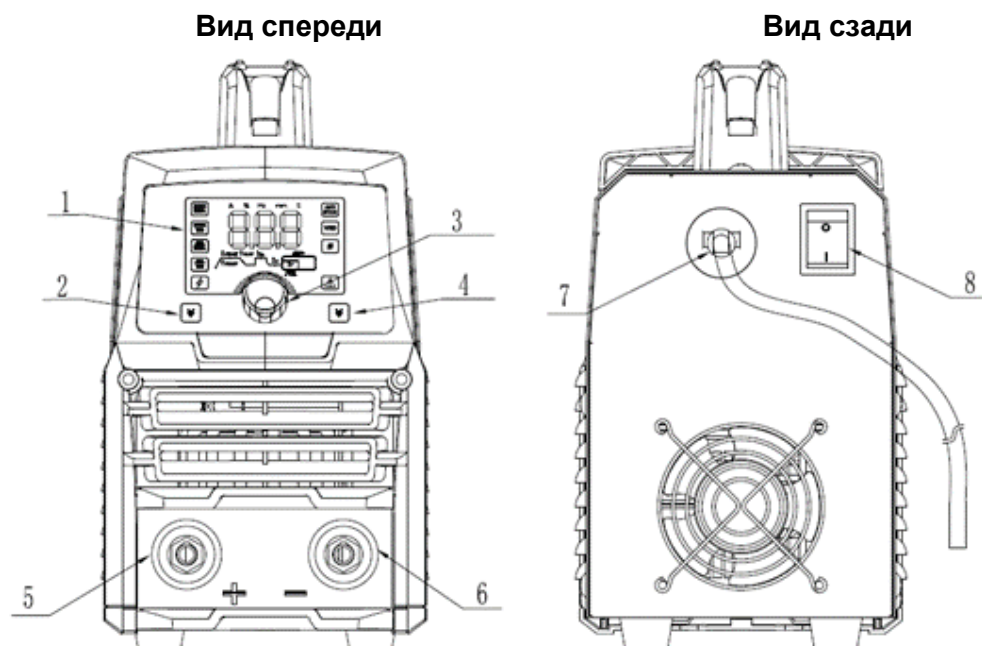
Общий вид (Инверторный сварочный аппарат постоянного тока MMA)
